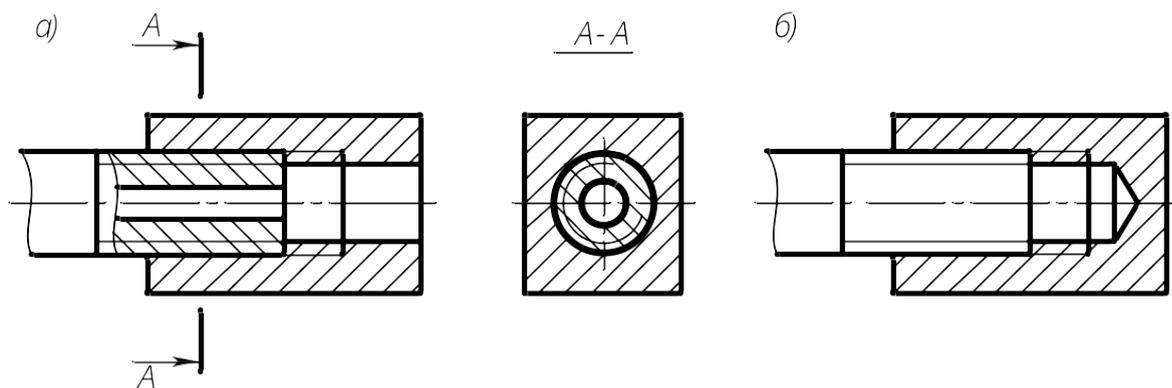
Изображение резьбы на чертежах в резьбовых соединениях
